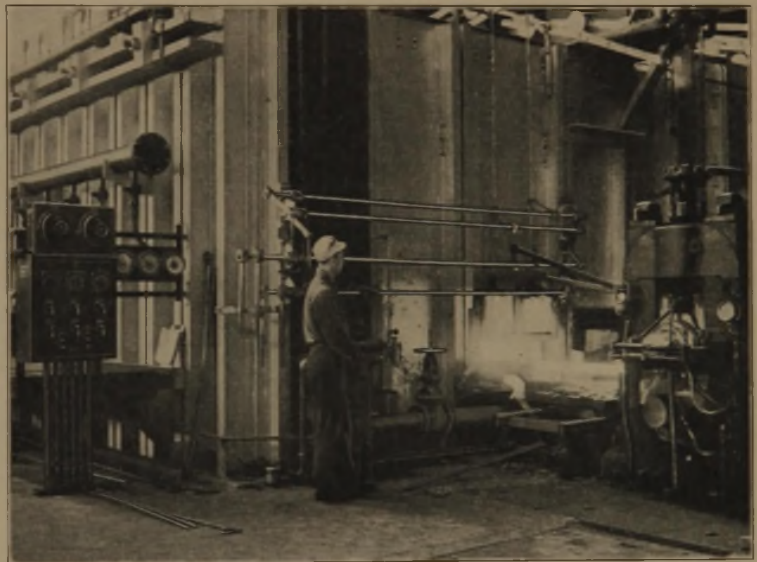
Ausstoßende eines Drahtknüppelofens mit unmittelbar davor stehendem Walzgerüst.
